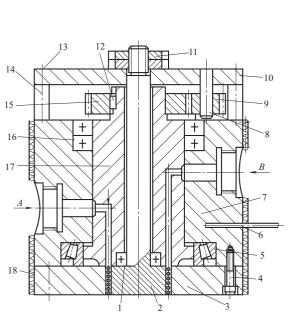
耐压塑料弹簧管机头 1—推力轴承 2—芯轴 3—压环 4—螺钉 5—圆锥滚子 轴承 6-热电偶 7-机体 8-轴 9-小齿轮 10-支板 11--锁紧螺母 12--键 13--内六角圆柱头螺钉
